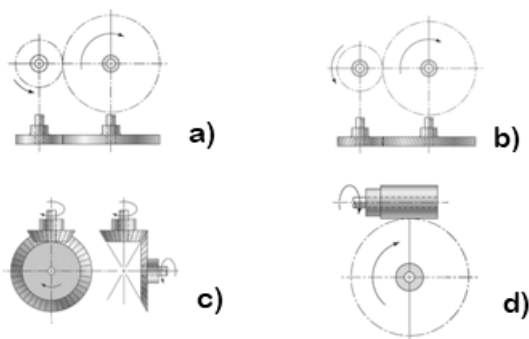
1 - a) Engrenagem cilíndrica dentes retos b) Engrenagem cilíndrica dentes helicoidais c) engrenagem cônica d) Engrenagem Sem-fim [2]
